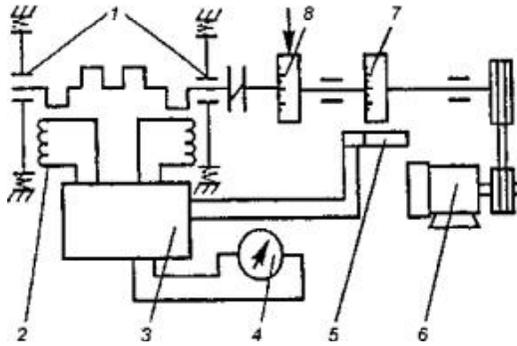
Схема машины для динамической балансировки коленчатых валов:
